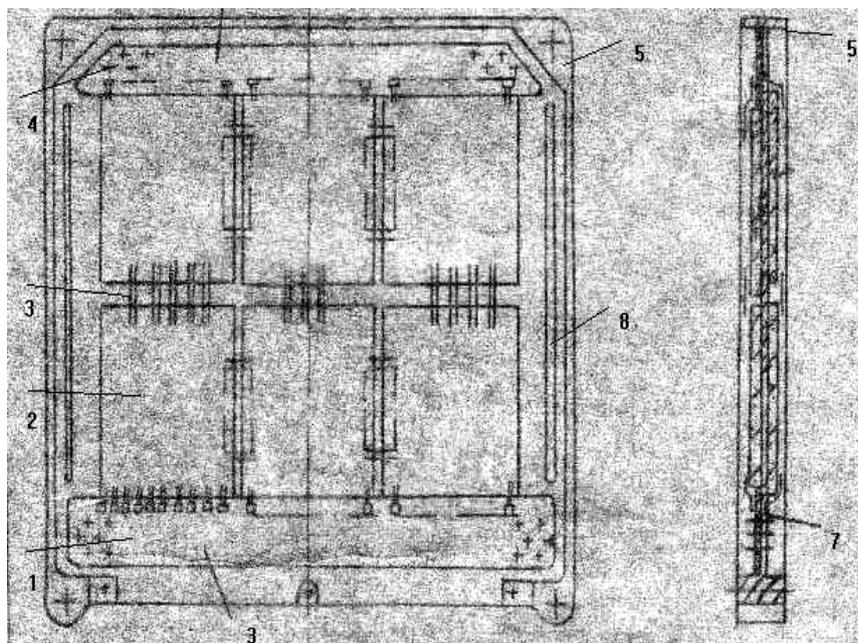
Конструкция двухсторонней ФЯ на металлической рамке: 1 - нижняя печатная вставка; 2 - МСБ; 3 - соединительный проводник; 4 - верхняя печатная вставка; 5 - рамка; 6 - планка; 7 - штырь; 8 - выступ
